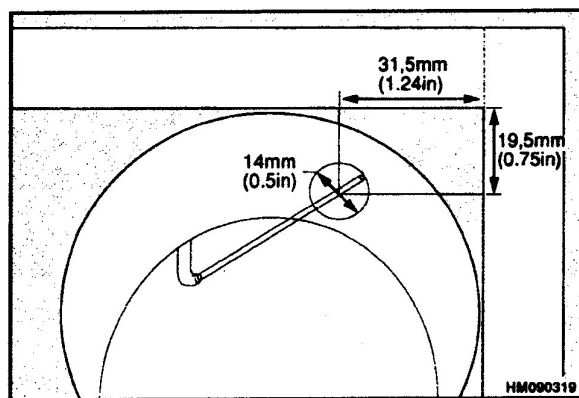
Регулировка сопла охлаждения поршня, двигателя типа AR.
